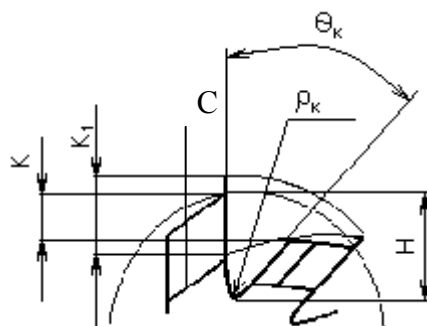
Форма зубця і стружкової канавки затилюваної фрези
